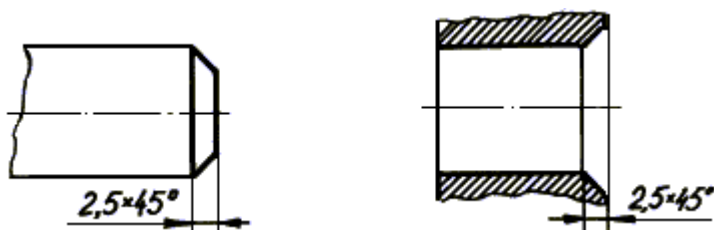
Нанесение размеров фаски, снятой под углом 45°
